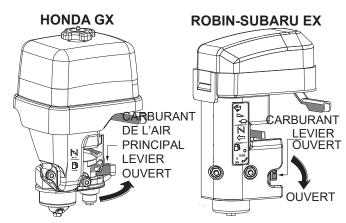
Levier de la valve d'essence du moteur (OUVERT)
